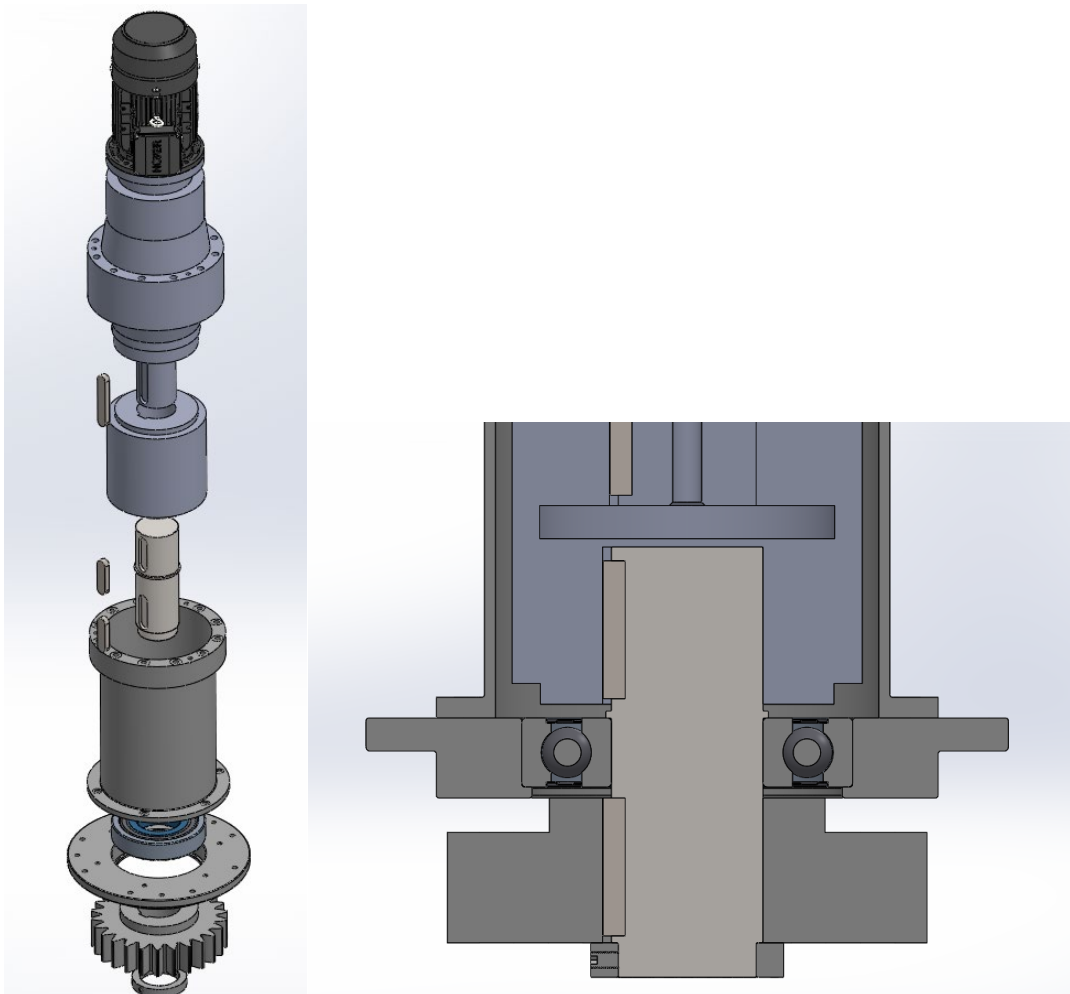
Detalles de conjunto despiezado y corte del sistema de giro.
